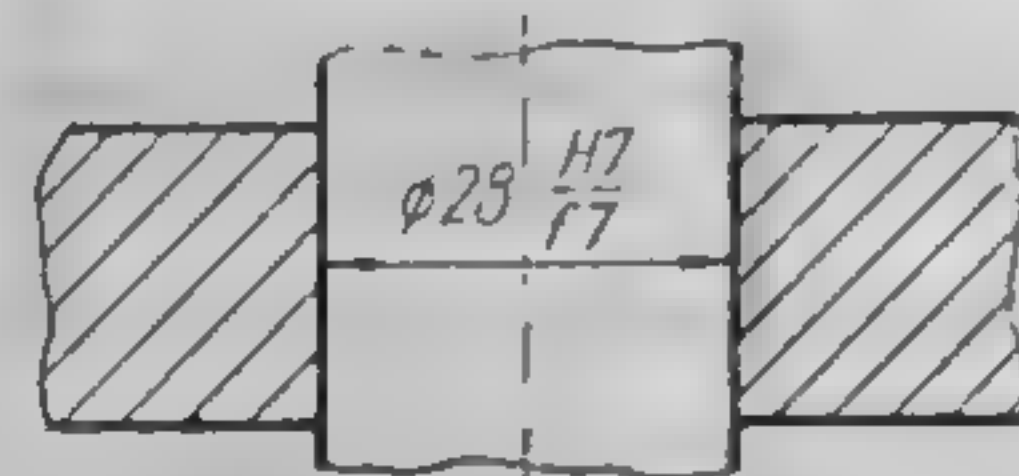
Înserierea toleranței la dimensiunea nominală a ajustajului prin simbolurile celor două câmpuri de toleranță sub formă de fracție, cu linia de fracție orizontală :
